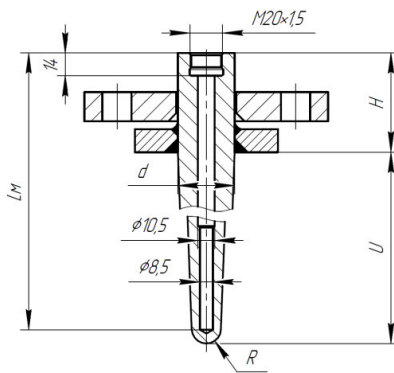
ГТ-714 для ДТ с неподвижным штуцером
